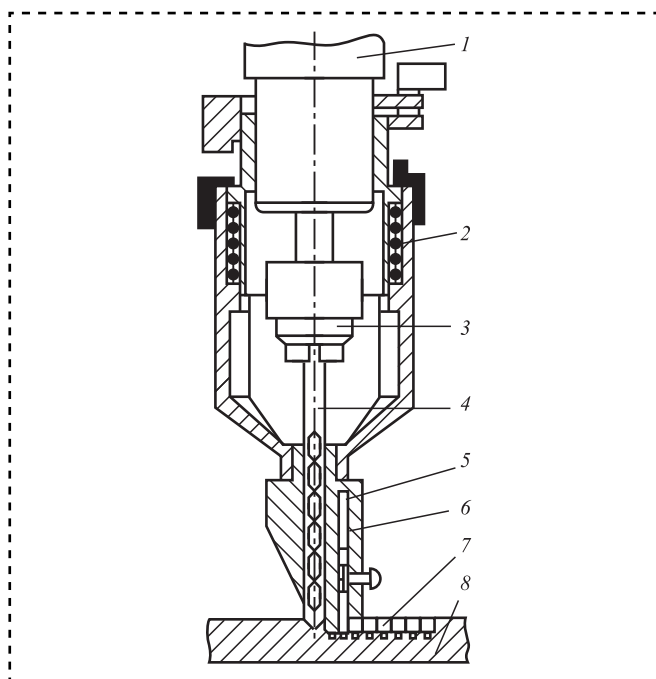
Кондуктор для сверления отверстий под фигурные вставки:
